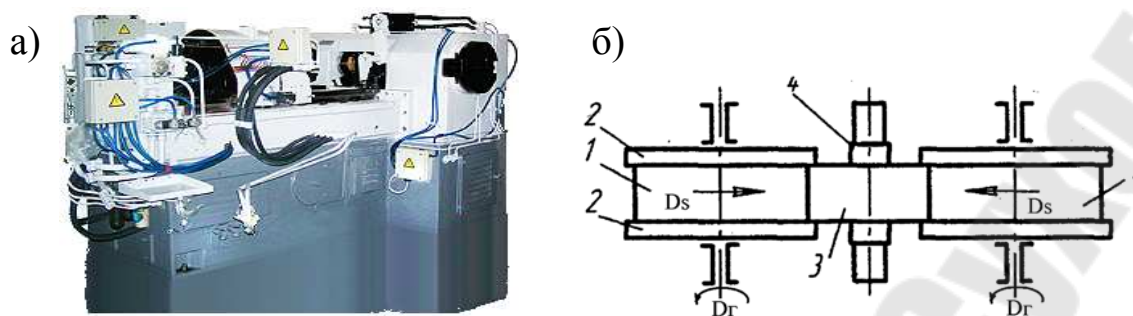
Общий вид шлице-зубонакатного станка (а) и схема накатки зубчатого колеса (б)
